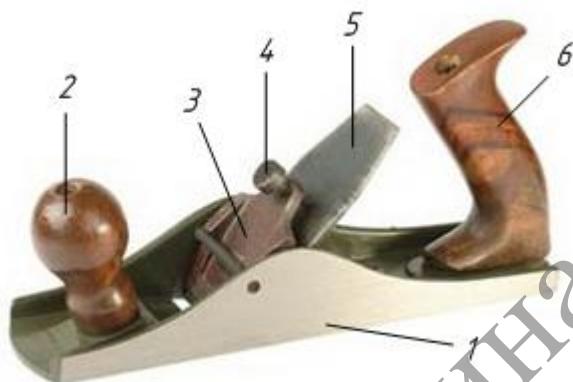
Устройство металлического рубанка с одиночным ножом
